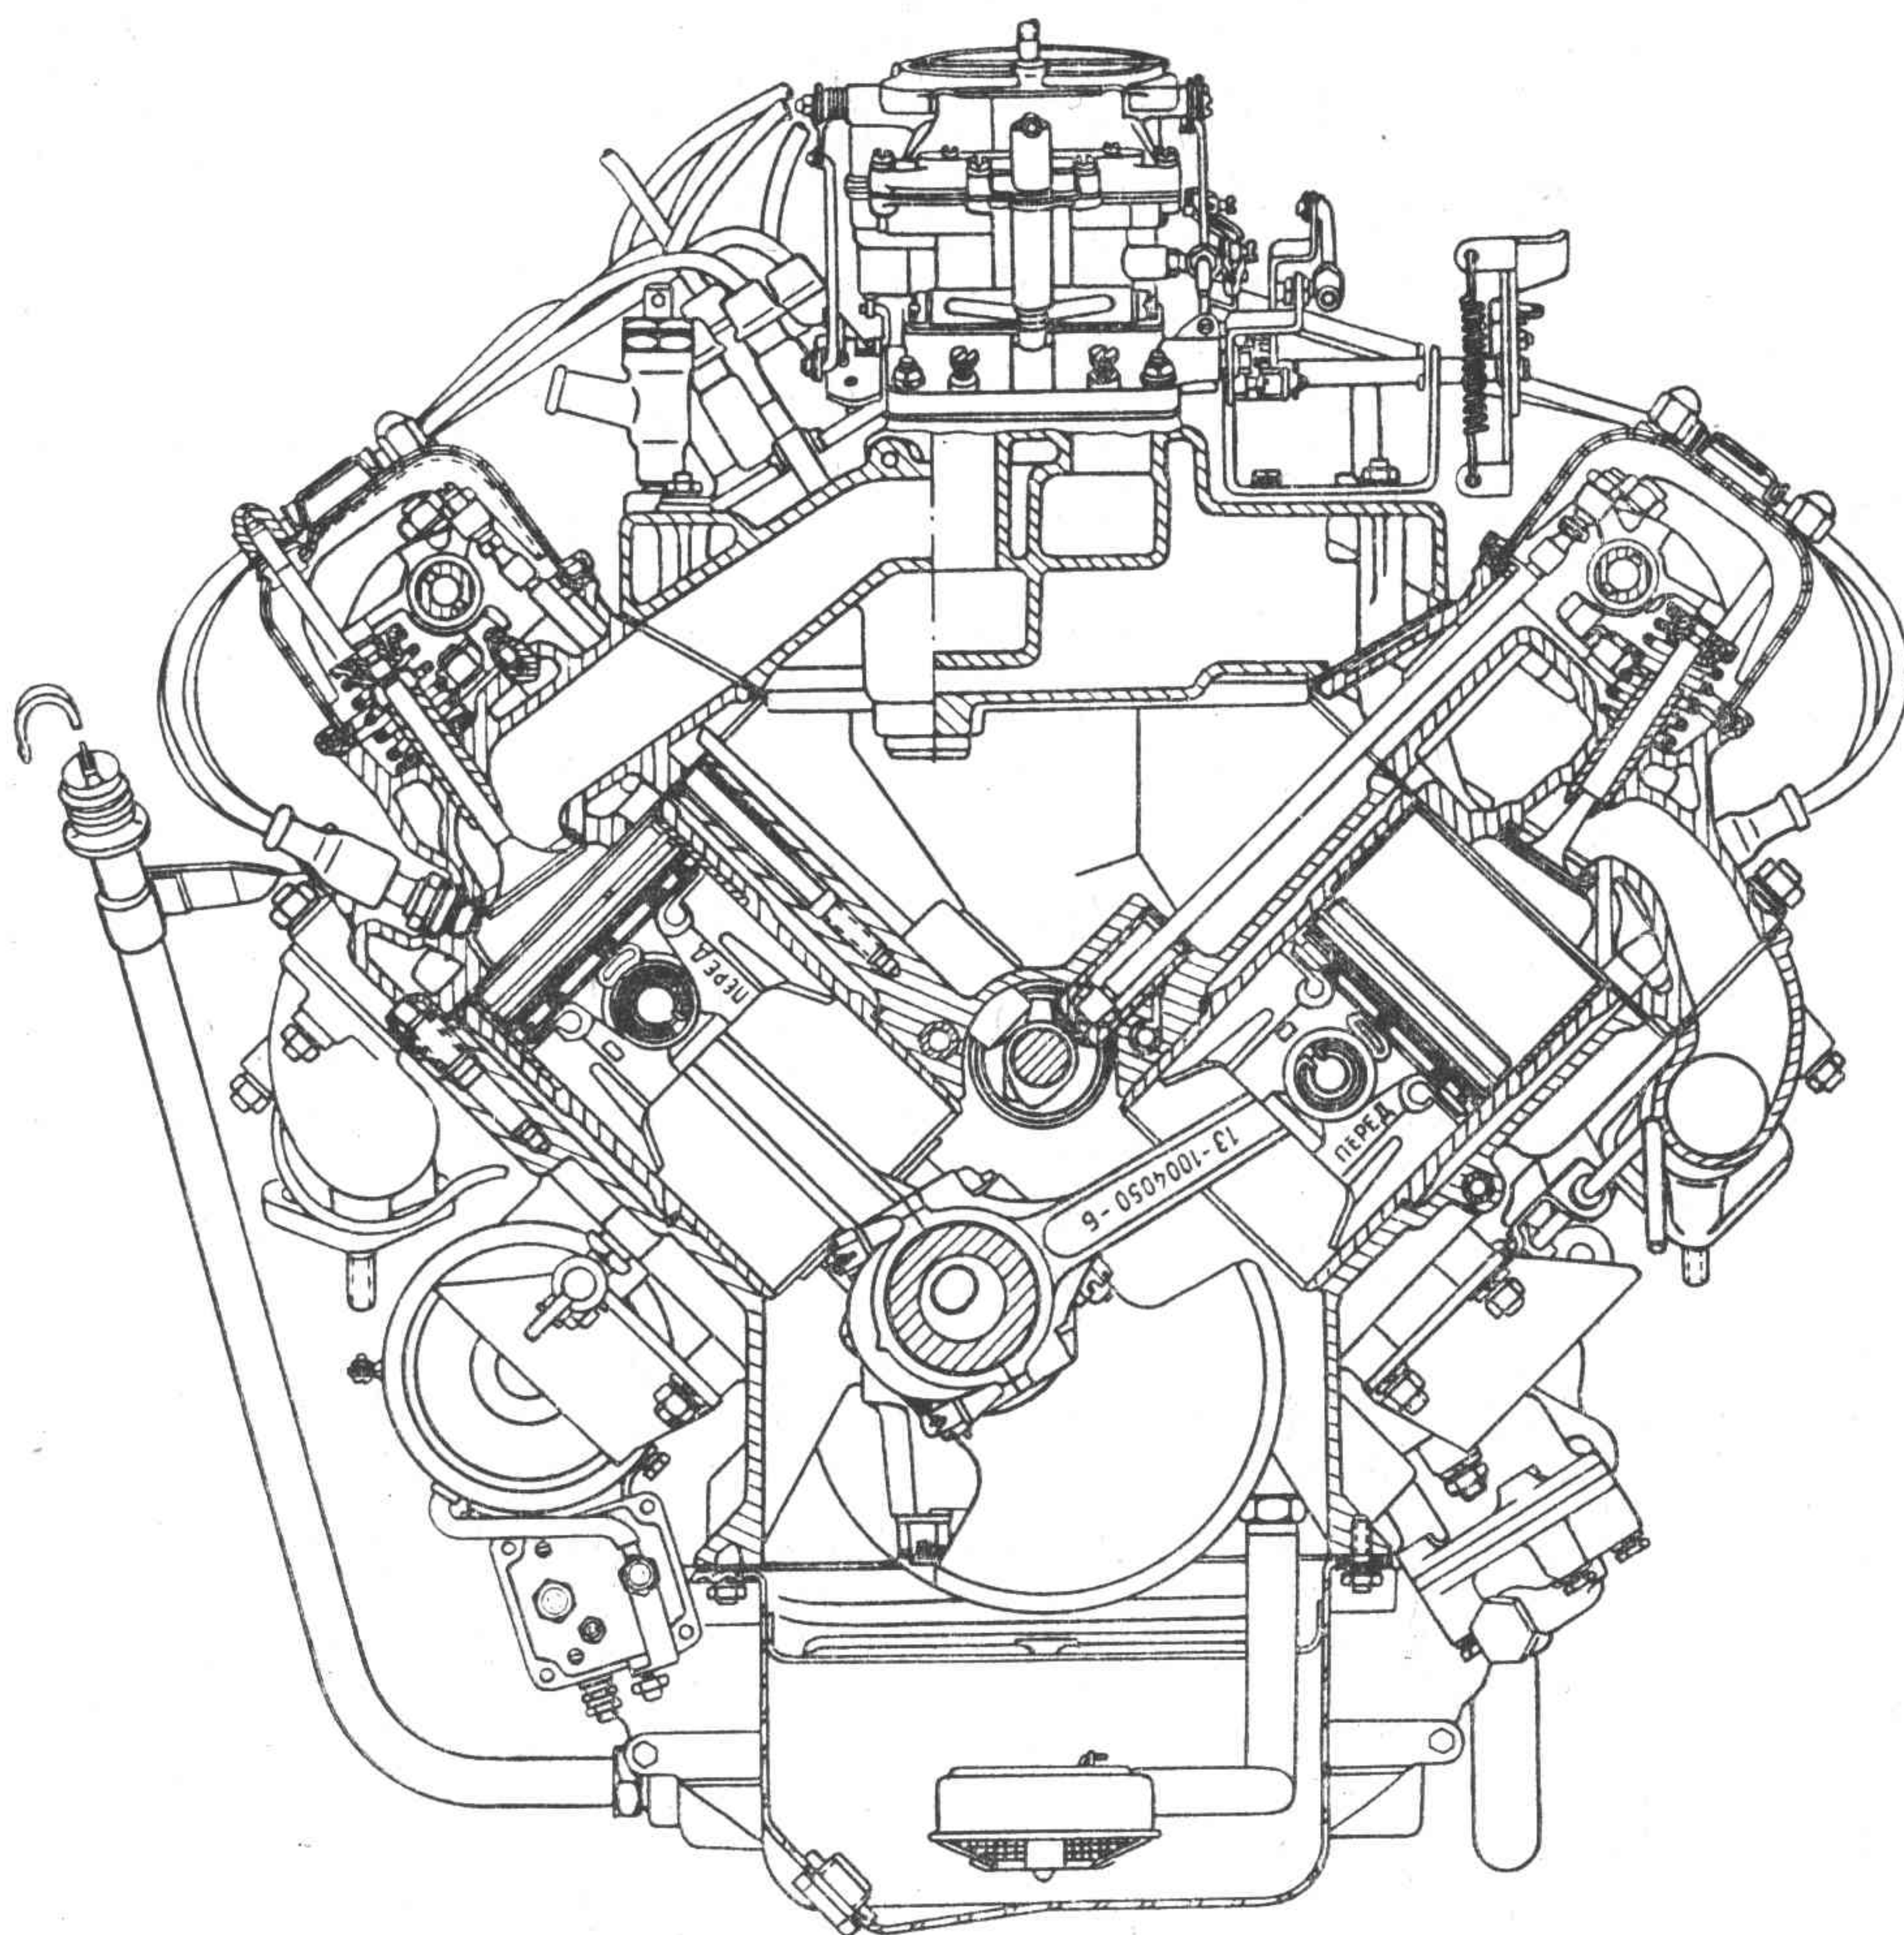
Поперечный разрез двигателя ГАЗ-13
